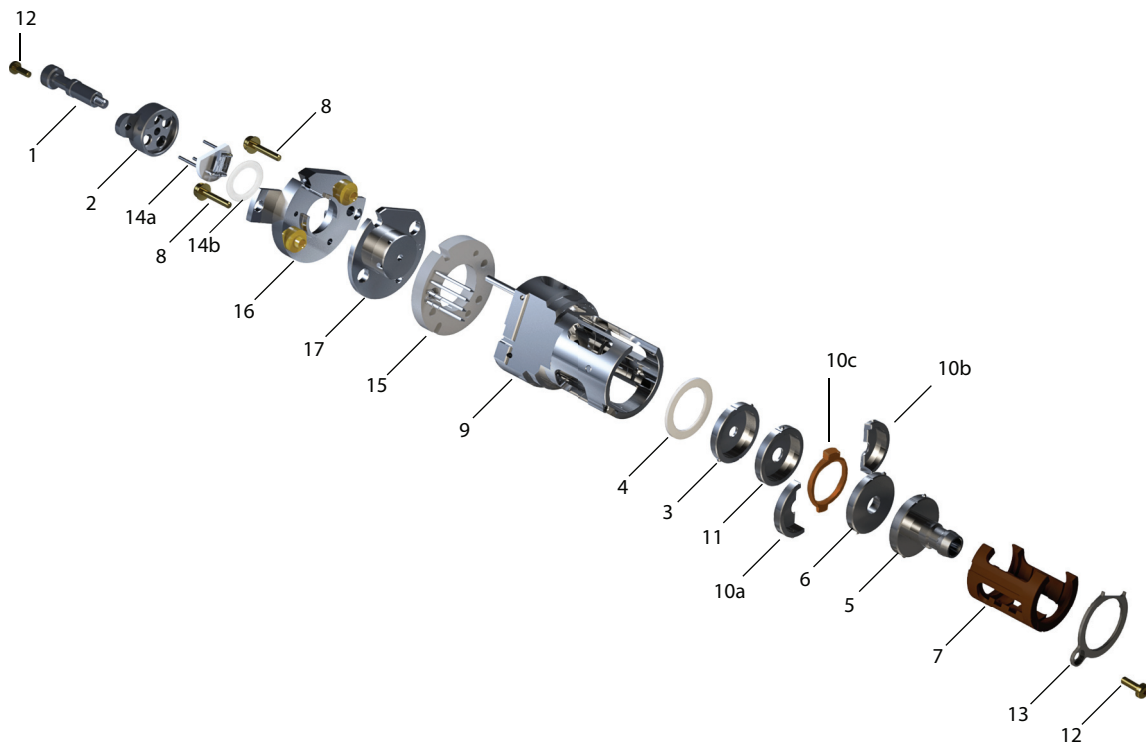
Vue éclatée des pièces de la source EI HES 2.0
